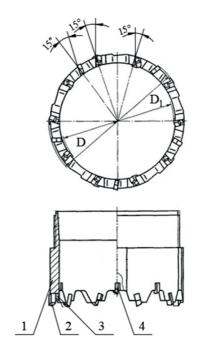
Твердосплавная коронка типа СТ2: 1 – корпус коронки; 2 – твердосплавная пластинка Г5107; 3 – вкладыш; 4 – твердосплавная пластинка Г5108; D – наружный диаметр; D_1 – внутренний диаметр
